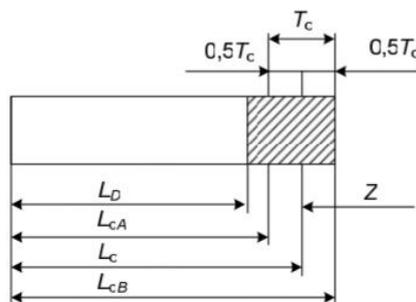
Взаимосвязь между номинальным размером до обрабатываемой поверхности детали, номинальным, предельными размерами отливки, припуском на сторону на обработку резанием и допуском отливки [3, с. 27]
